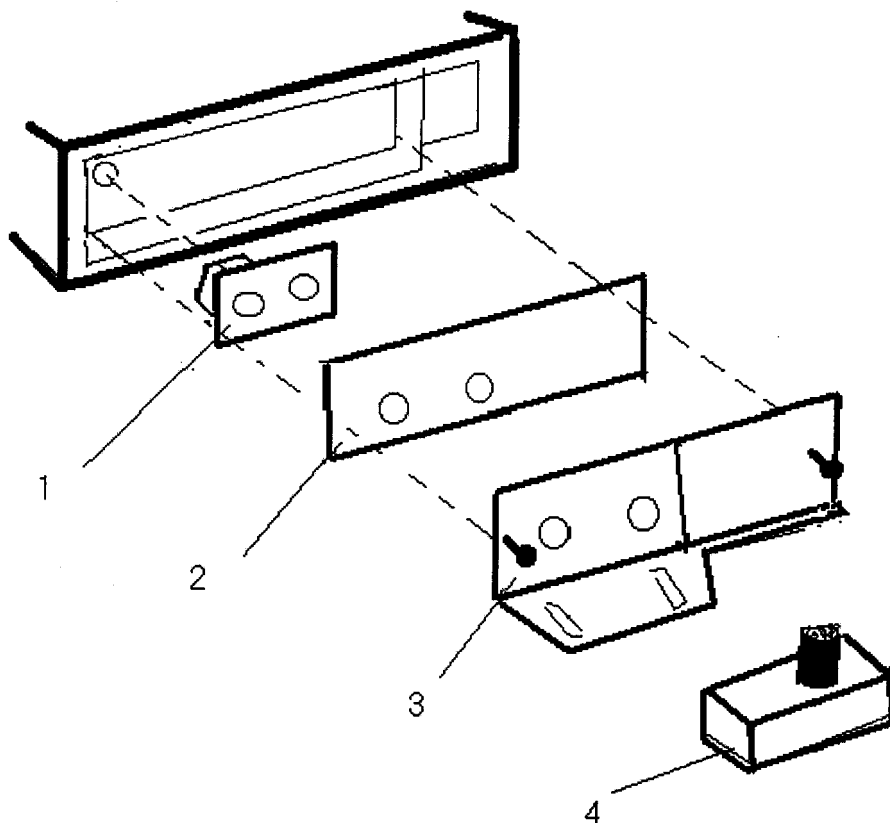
Порядок установки увлажнителя на инкубатор
